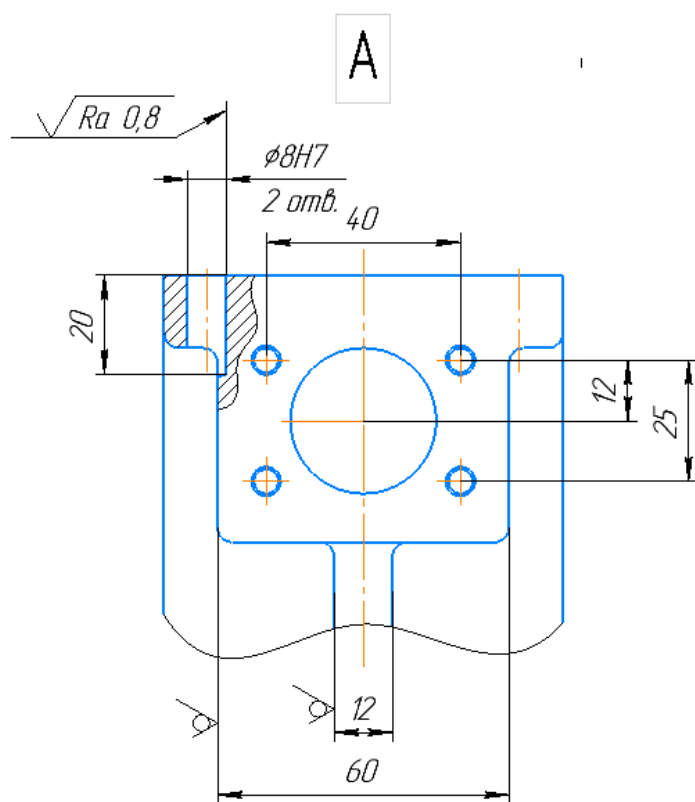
Чертеж детали 2 до метрологической экспертизы (вид А)
